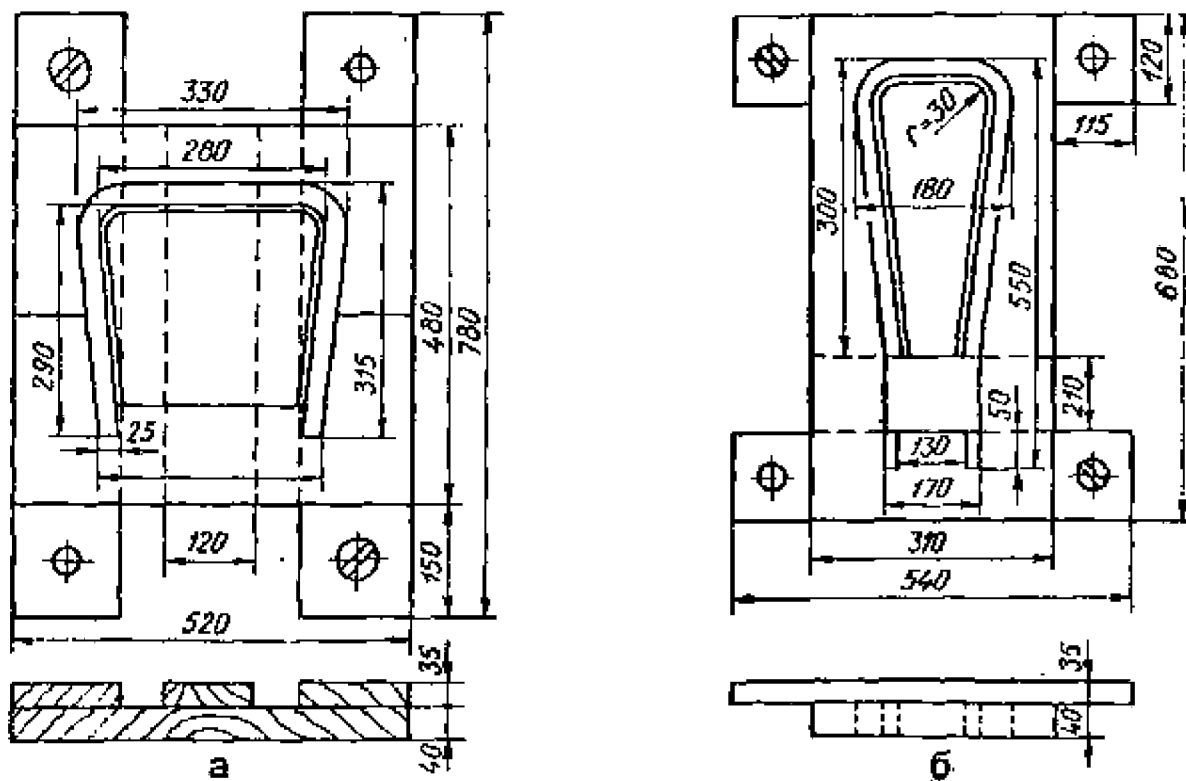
Шаблоны для гнутья деталей (размеры в миллиметрах): а - кольцевых; б - трапециевидных
